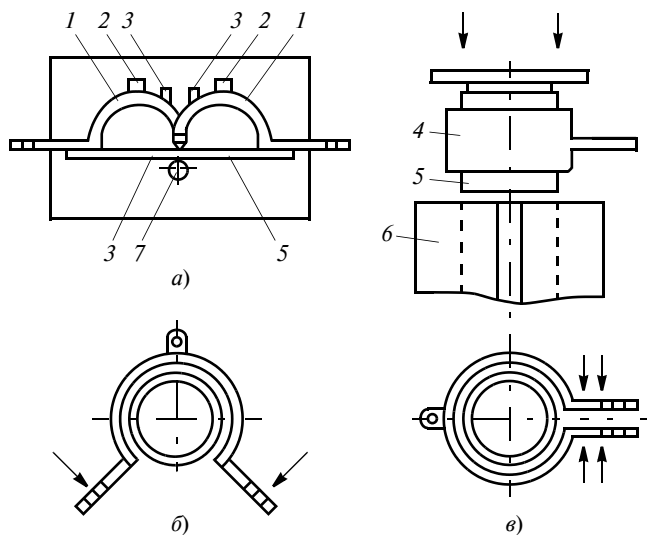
Захват для свёртывания и ввода пластины в пресс-форму:
